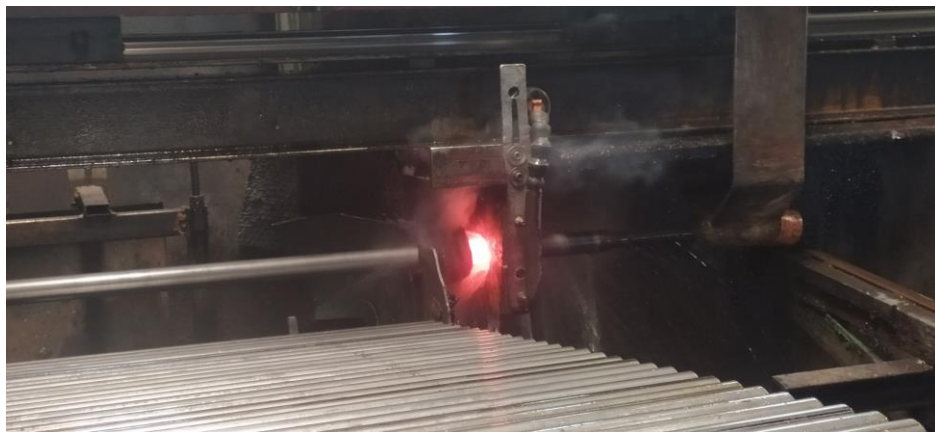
Трубная заготовка, проходящая через индуктор и спрейер
